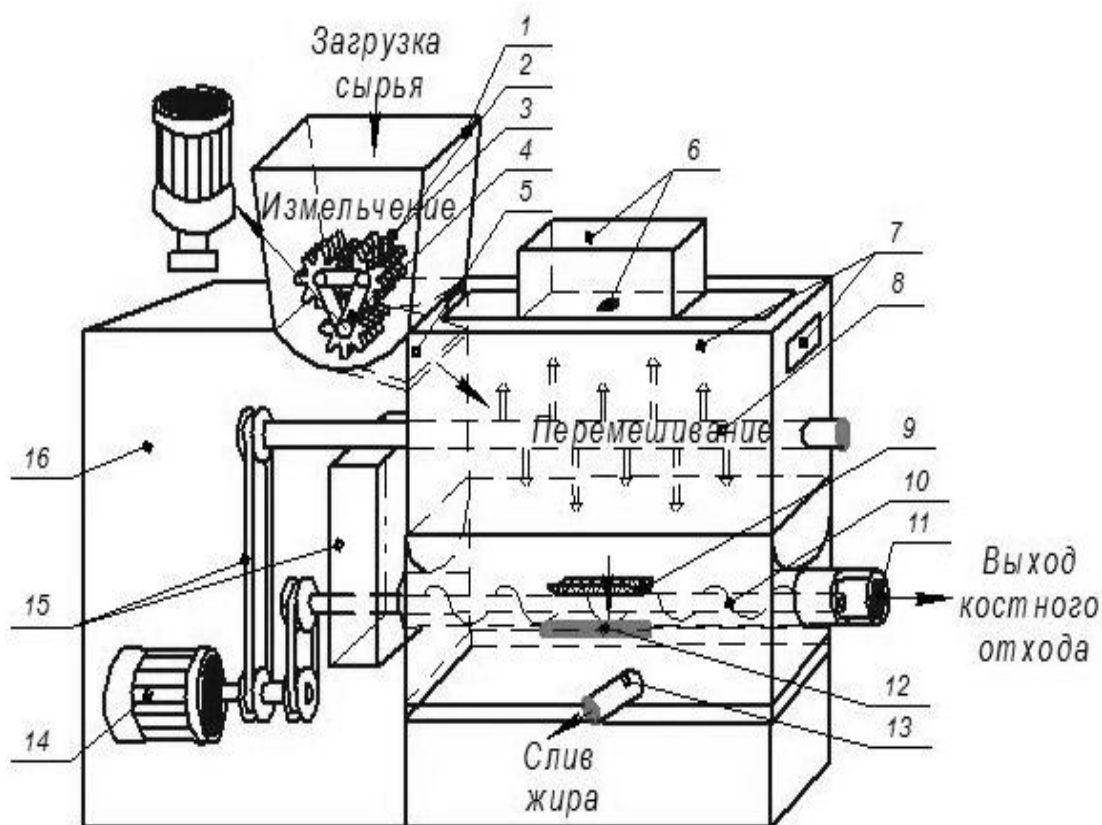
Установка для термообработки жиросодержащего сырья: 1 – загрузочная емкость; 2 – вальцовый измельчающий механизм; 3 – набор звездочек с электродвигателем; 4 – электродвигатель с передаточным механизмом; 5 – лоток; 6 – СВЧ генератор; 7 – резонаторная камера; 8 – привод перемешивающего механизма; 9 – окно корпуса нагнетательного шнека; 10 – нагнетательный шнек; 11 – матрица; 12 – фильтр; 13 – приемная емкость; 14 – электродвигатель; 15 – ременная передача и редуктор; 16 – экранирующий корпус
